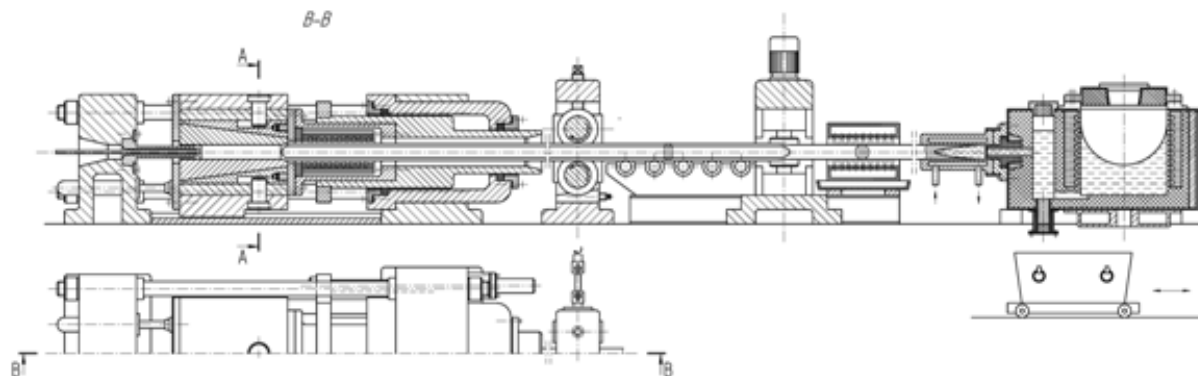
Конструктивный вариант литейно-прессового агрегата на базе горизонтальной МНЛЗ и трубо-профильного пресса
